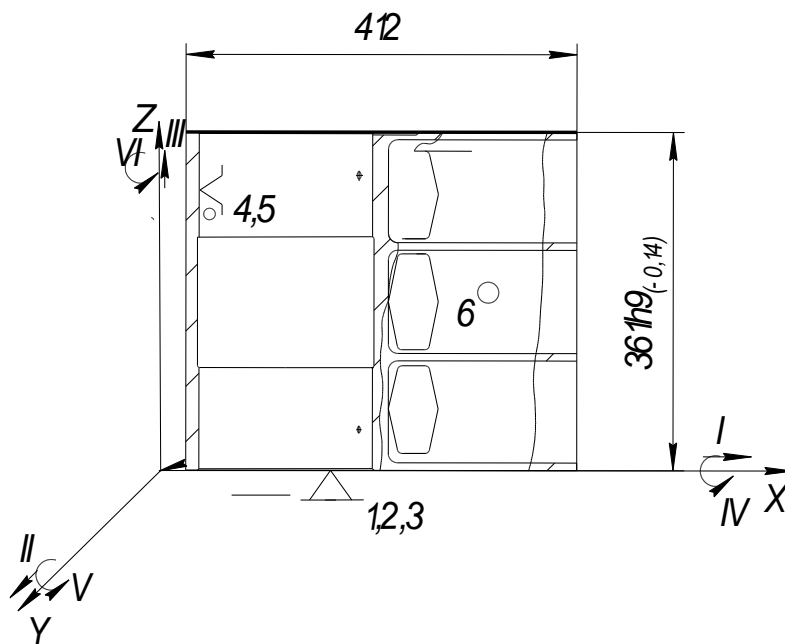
Схема базування на фрезерній операції (Установ Б).
